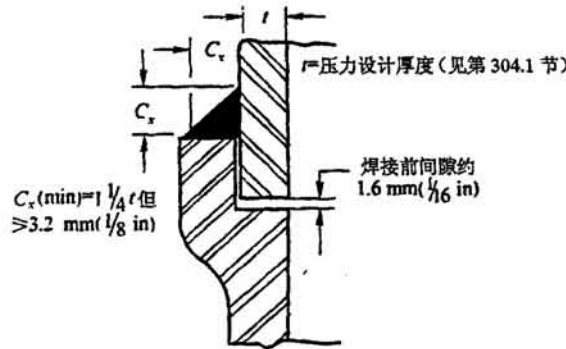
C 除法兰外的承插焊组件的最小焊接尺寸
